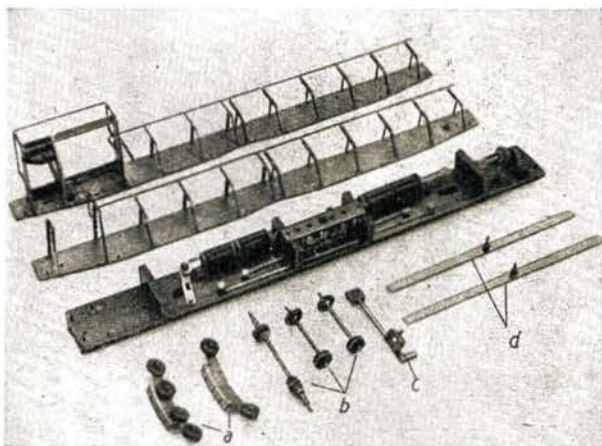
Langträger mit Schutzausträger und Bühnengeländer, Hauptträger mit Doppelspulenmagneten, Querträger und Schleifkontaktträger; a Laufwerk, b Getriebegruppen, c Signalbaugruppe, d Riegel mit eingelöteter Schraube M 2 x 10
